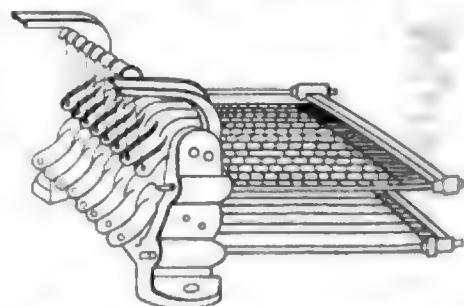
Z. A. Simplex-Schaftmaschine mit Schräghebel für Holzkarten.
